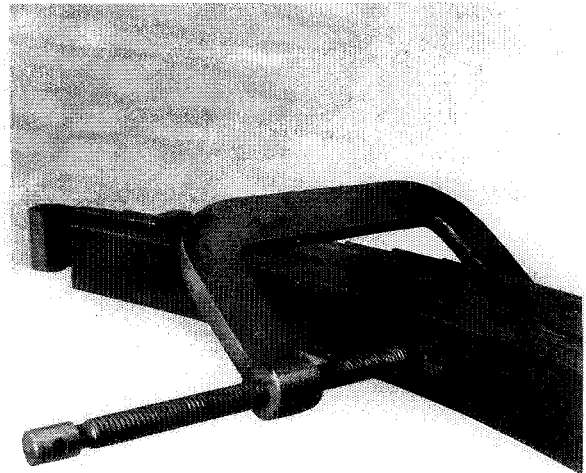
Mit einer Schraubzwinde zusammengespante Hinterradfeder
